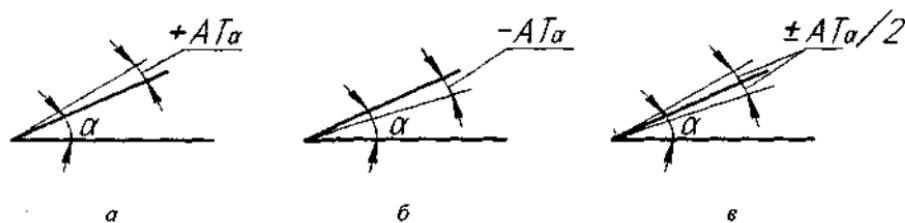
Типы расположения полей допусков для угла призматического элемента:
